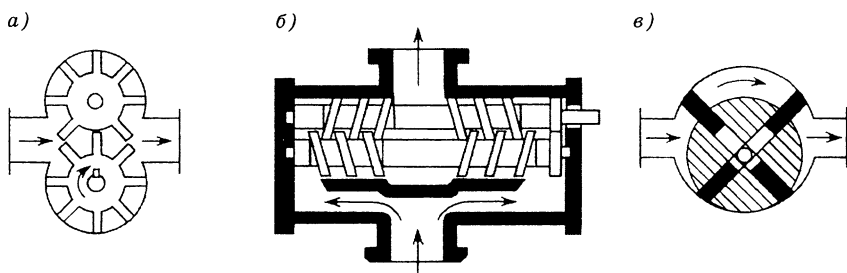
Схемы устройства роторных насосов: а — шестеренного; б — винтового; в — пластиначного
